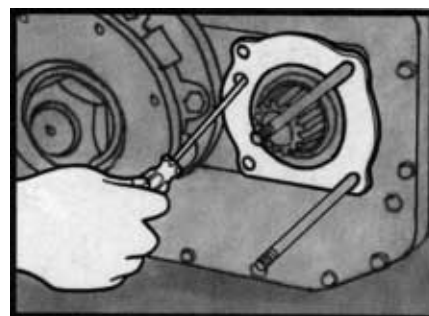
установка новой крышки корпуса подшипника и прокладки
